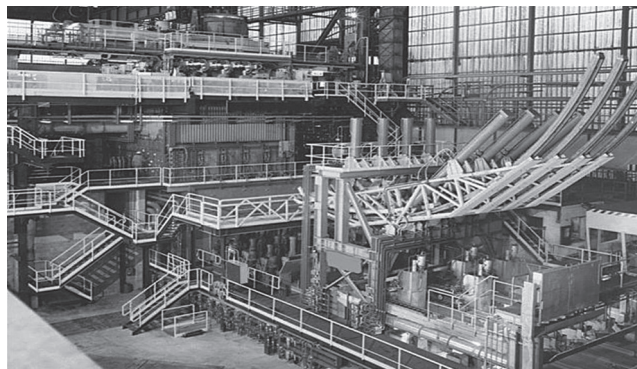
Схема современной машины непрерывного литья заготовок (скорость разли-
